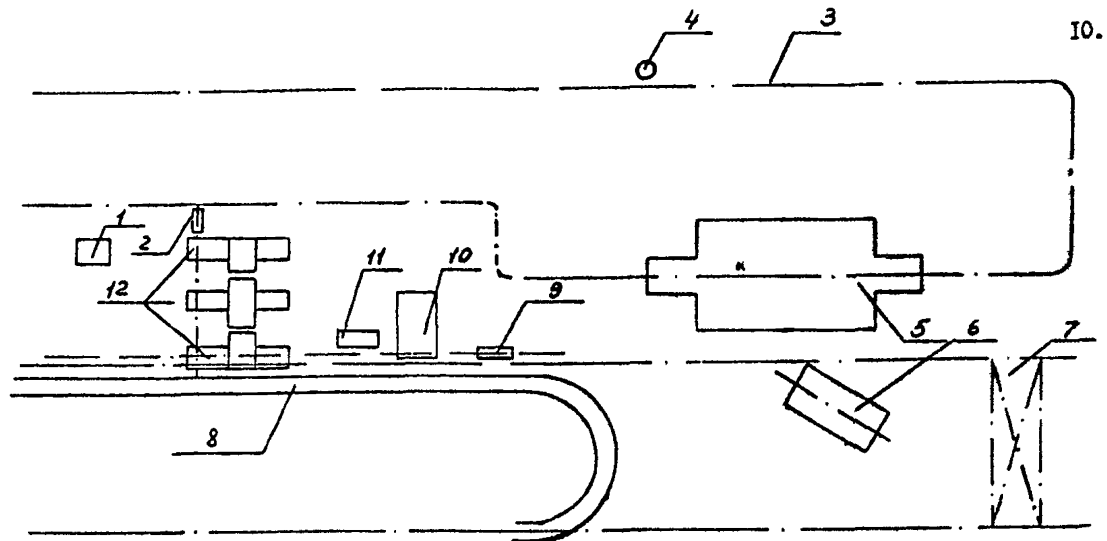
Типовая схема планировки рабочего места разборки двигателя
